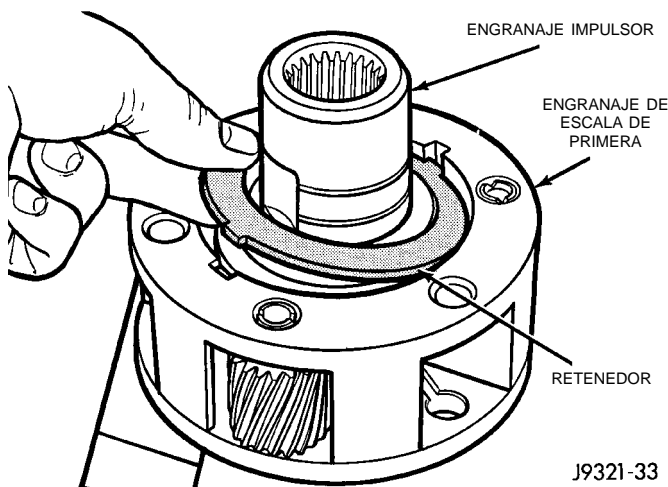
Desmontaje del retenedor del engranaje impulsor
